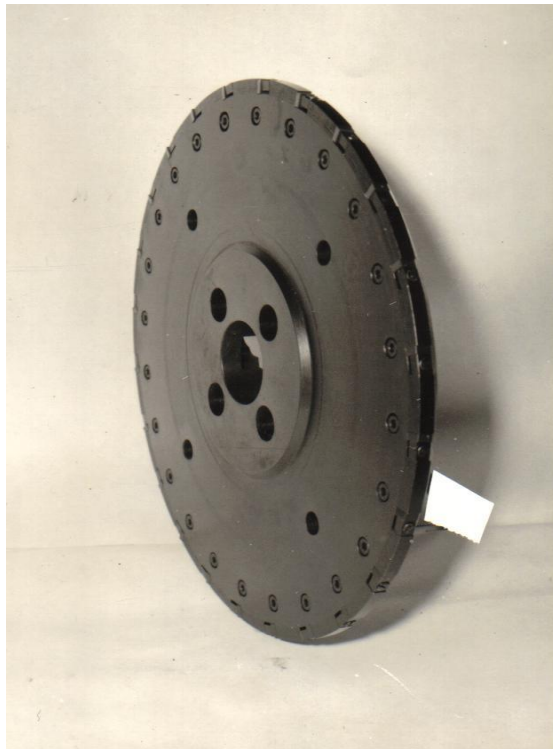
Конструкція дискової фрези однобічного різання
